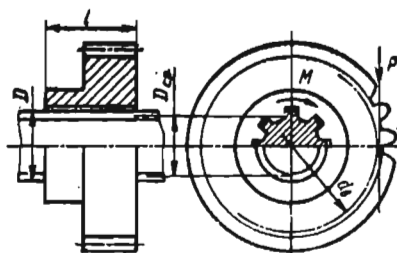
Соединение, передающее крутящий момент и окружное усилие (группа МР)
